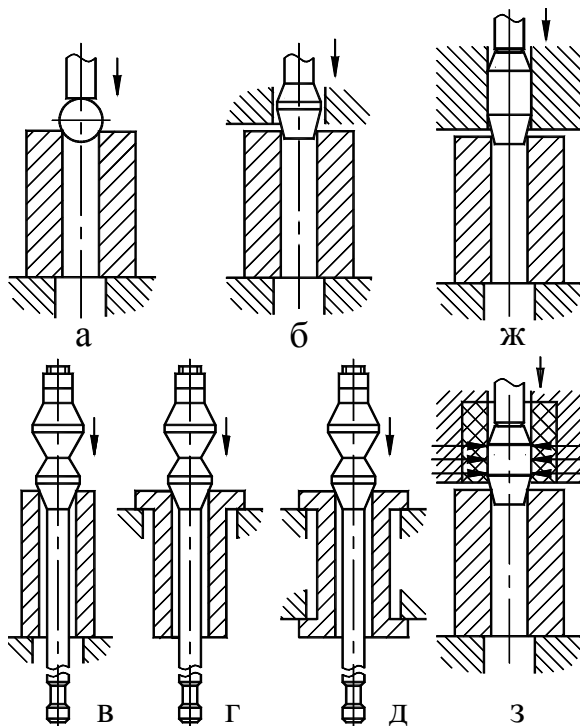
Схемы дорнования отверстий: а – шаром; б – консольно закрепленной однозубой прошивкой; в – многозубой протяжкой со сжатием заготовки; г – многозубой протяжкой с растяжением заготовки; д – многозубой протяжкой с осевым заневоливанием заготовки; ж – однозубой незакрепленной в осевом направлении прошивкой, размещенной с зазором в направляющей втулке; з – однозубой незакрепленной в осевом направлении прошивкой, размещенной с натягом в направляющей втулке
